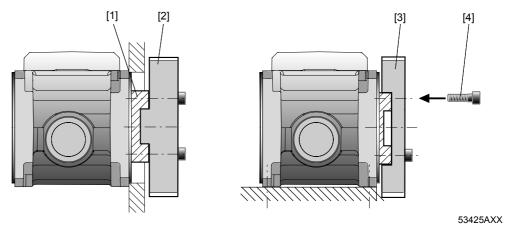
Exemplo de montagem para um bloco de flange BSBF..
